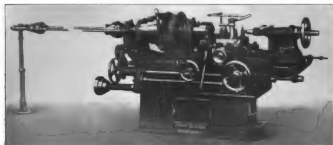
Maschine zur Herstellung von Stehbolzen (Werkzeugmaschinenfabrik Ernst Schieß).
